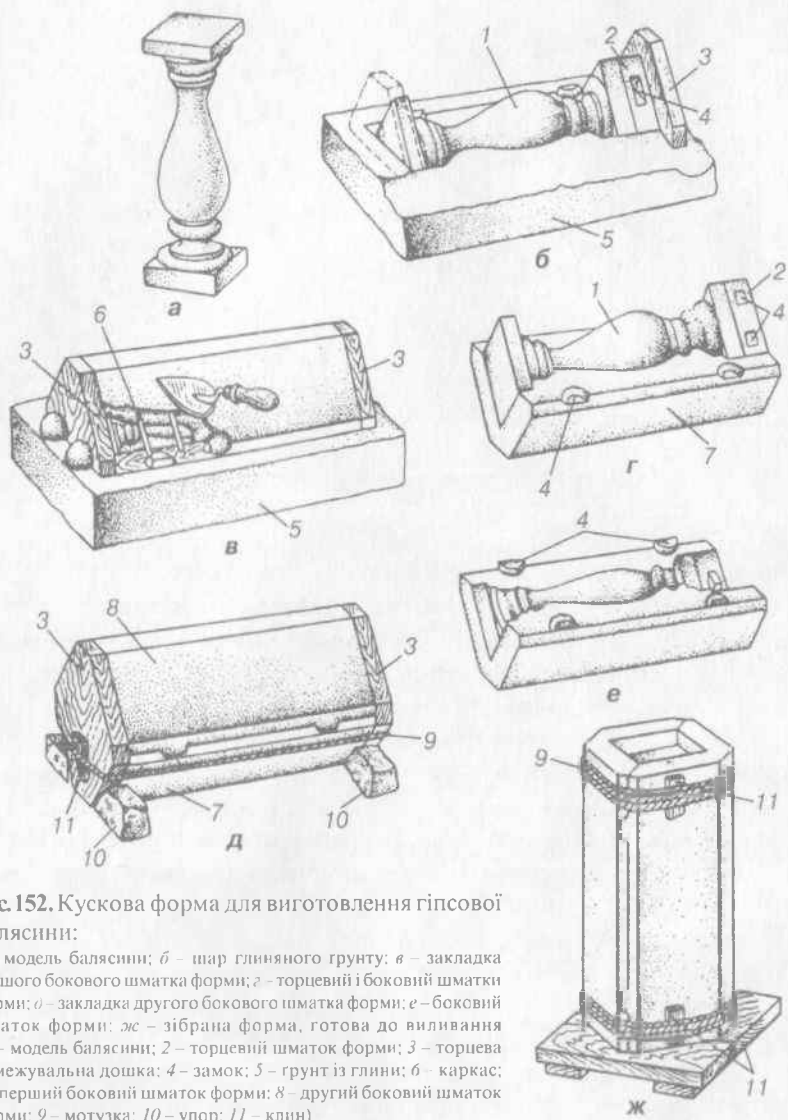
Кускова форма для виготовлення гіпсової балясини:
